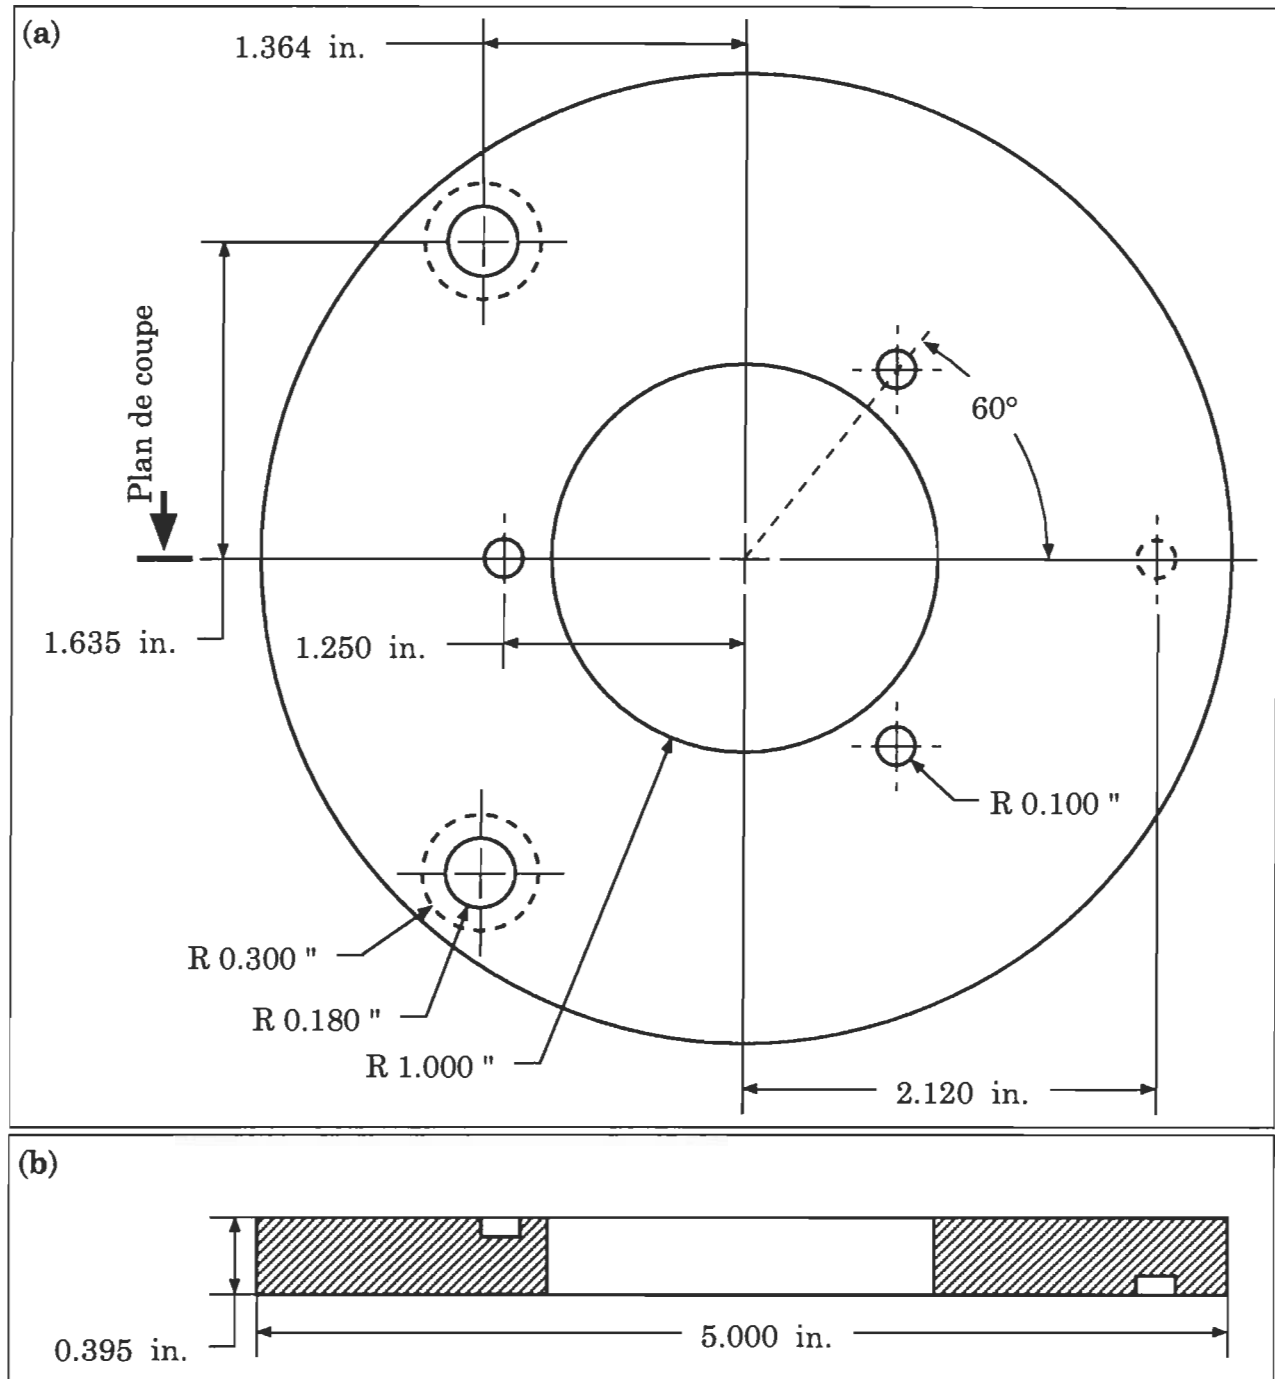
Vue de dessus [a] et vue de coupe [b] du support mobile de la tête AFM.
